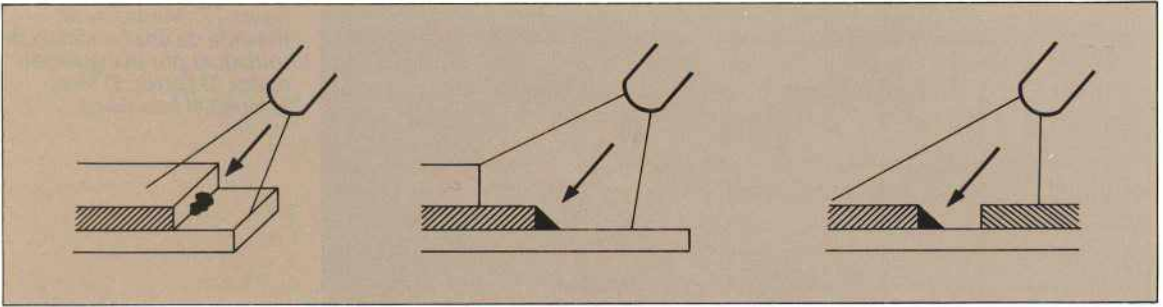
Sistema de seguimiento del cordón para palpar la hendidura sin que las soldaduras por puntos o los dispositivos de tensado perturben la medición.
